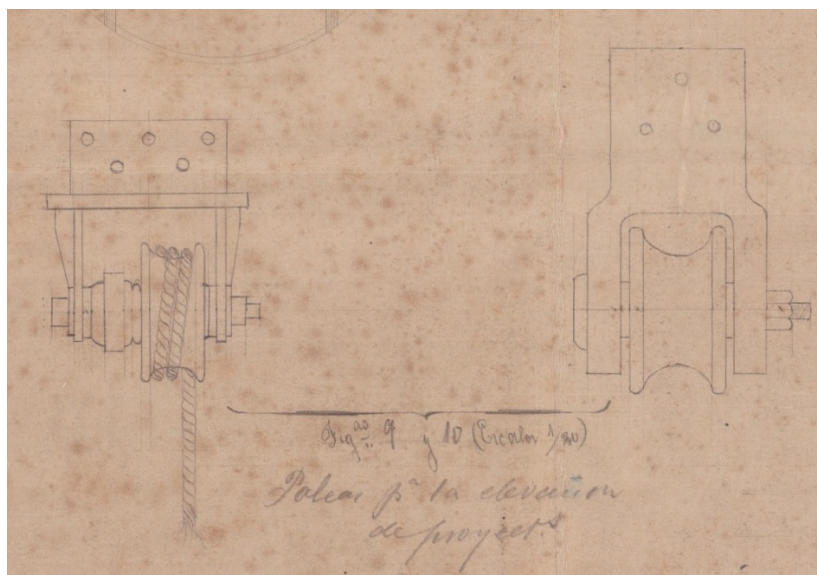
Detalles de las poleas para la elevación de proyectiles.
